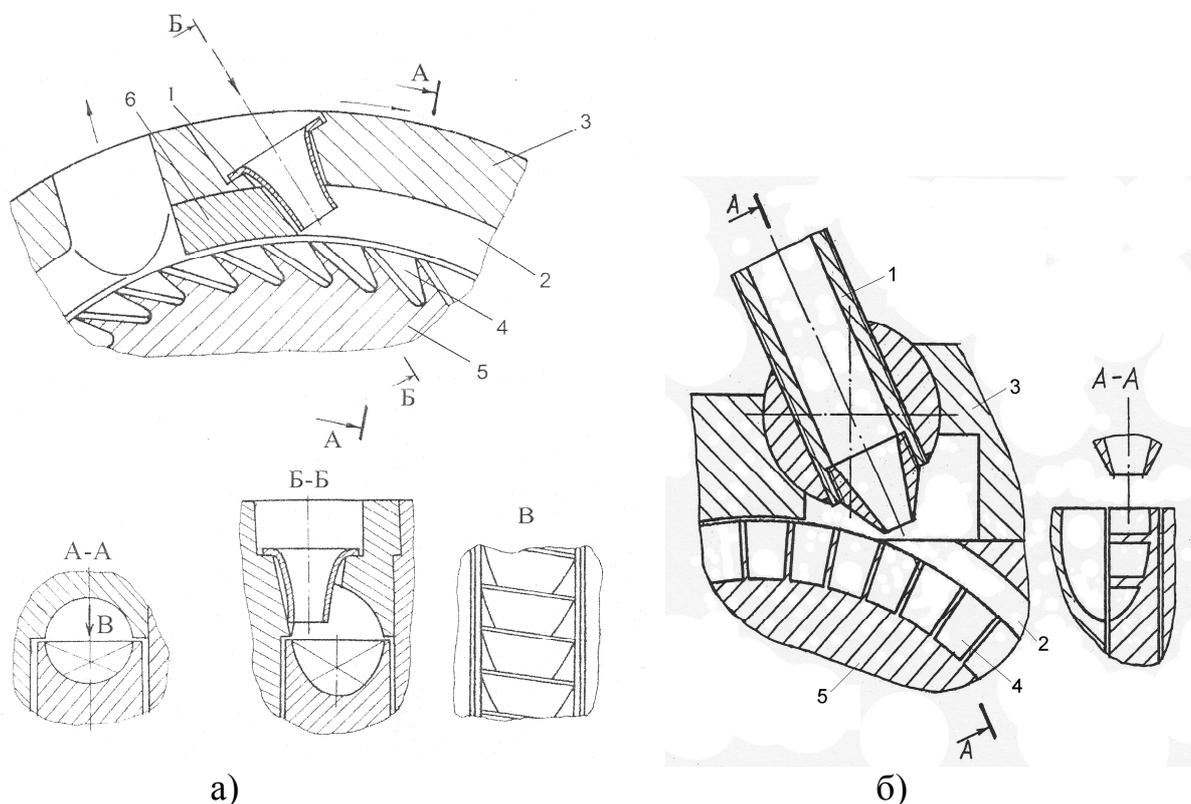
Конструктивная схема вихревой ступени:
